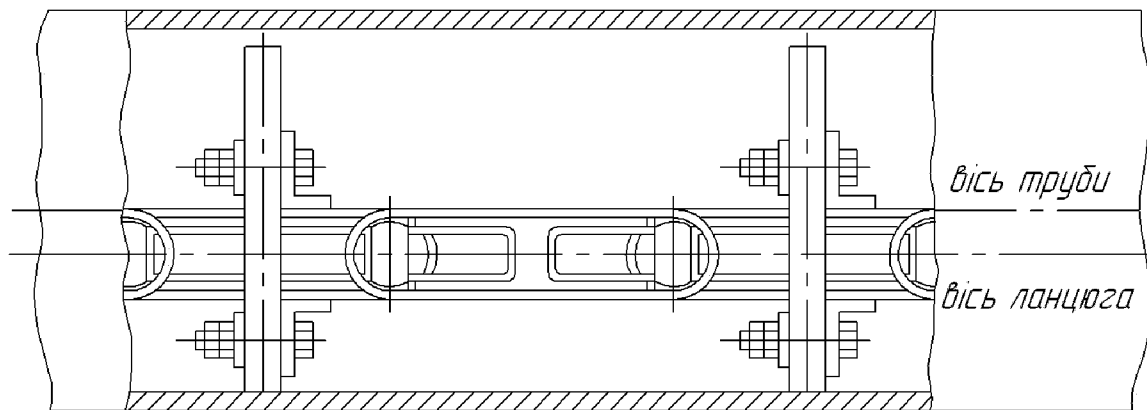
Схема робочих елементів трубного скребкового конвеєра
